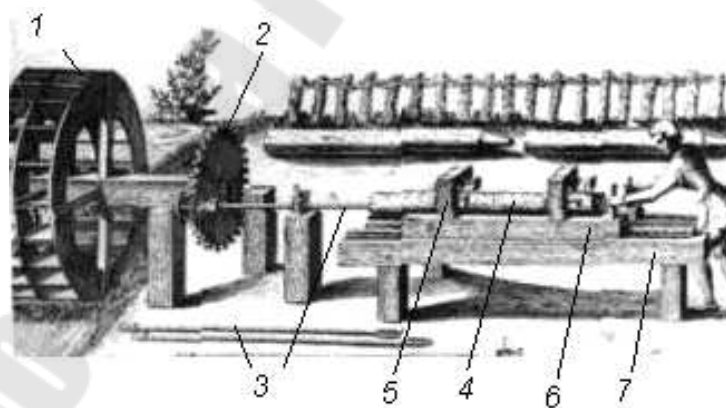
Сверлильный станок с гидромеханическим приводом: 1 – гидроколесо, 2 – зубчатая передача, 3 – сверло, 4 – заготовка, 5 – зажим, 6 – ручной суппорт (сани), 7 – станина.
